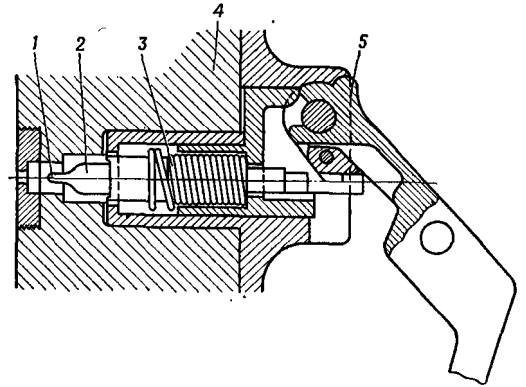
Схема устройства оружейного ударного механизма ударникового типа: 1 — боек; 2 — ударник; 3 — боевая пружина; 4 — затвор; 5 — рычаг взвода ударника.
